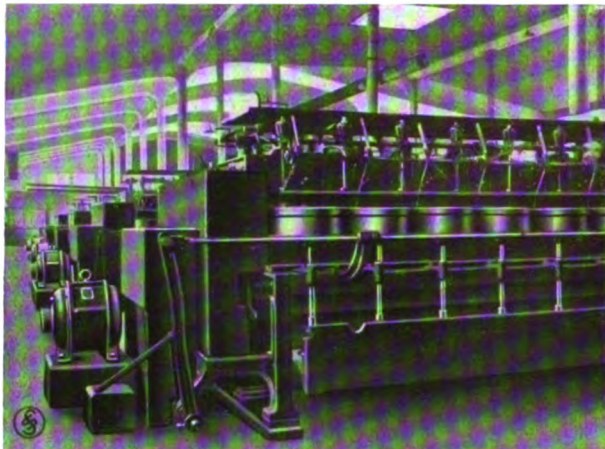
Schlauchkops-Spinnmaschinen, angetrieben durch Kurzschlußläufermotoren.
